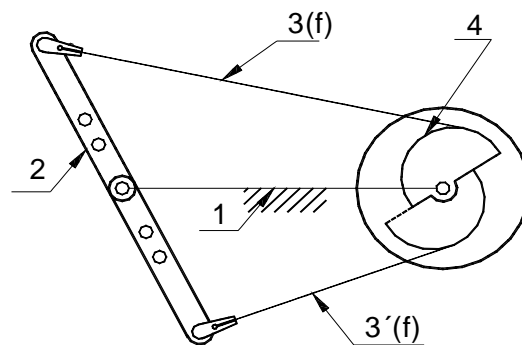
Tensionarea firului flexibil pe cale constructivă utilizând un montaj simetric
